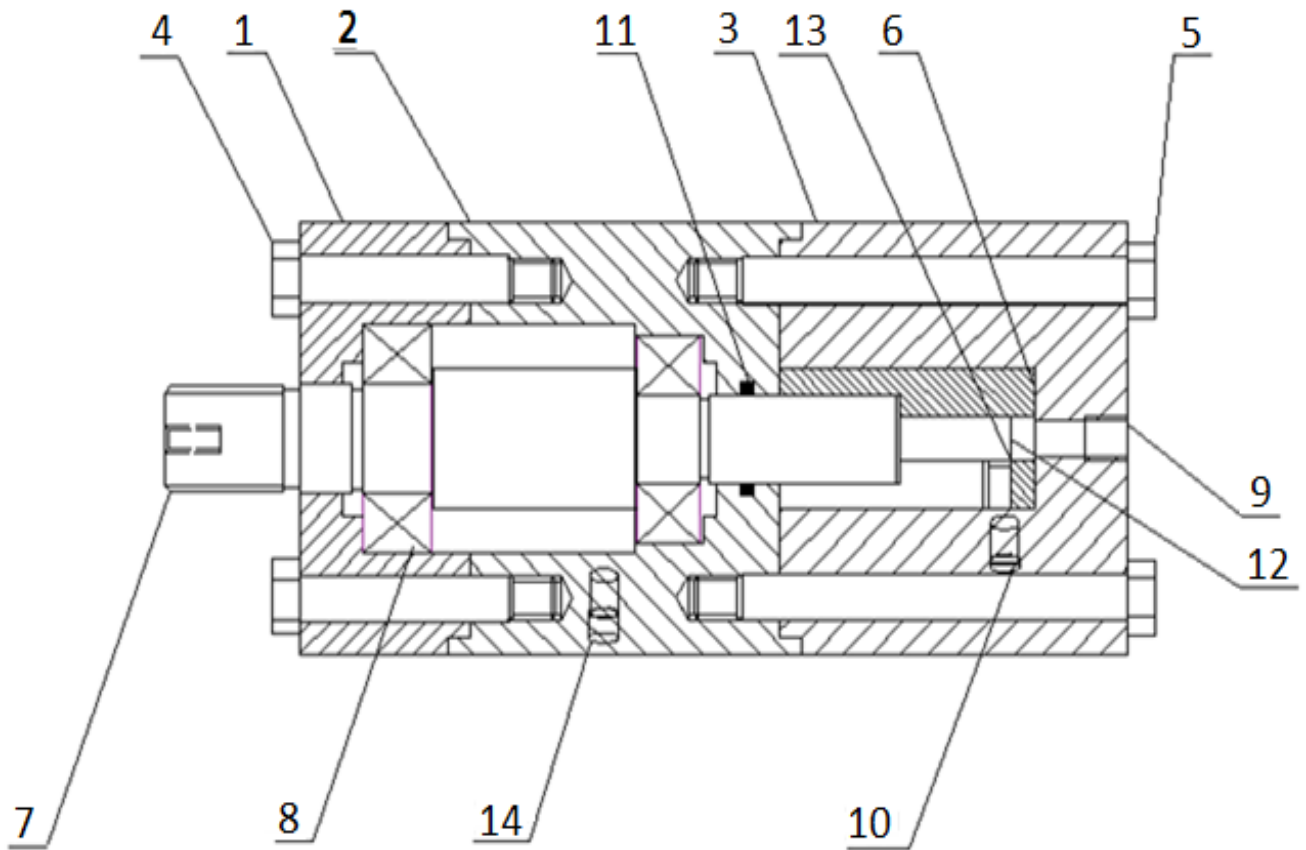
Загальна схема регульованого дроселя: 1 – корпус;
